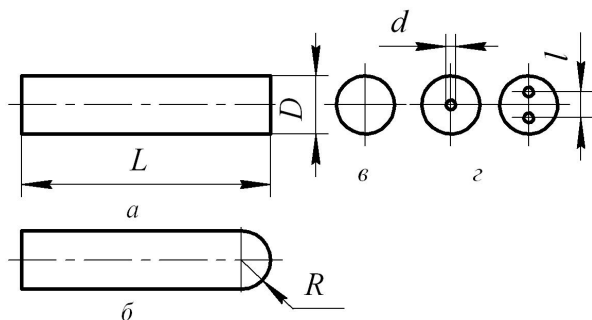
Форма твердосплавных заготовок-стержней:
